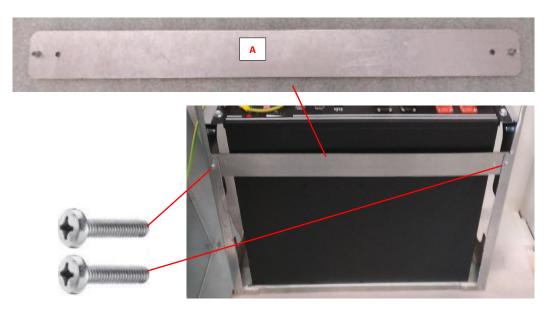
Instalación del soporte de separación de la batería en la BASE WALL-BOX-Bx
